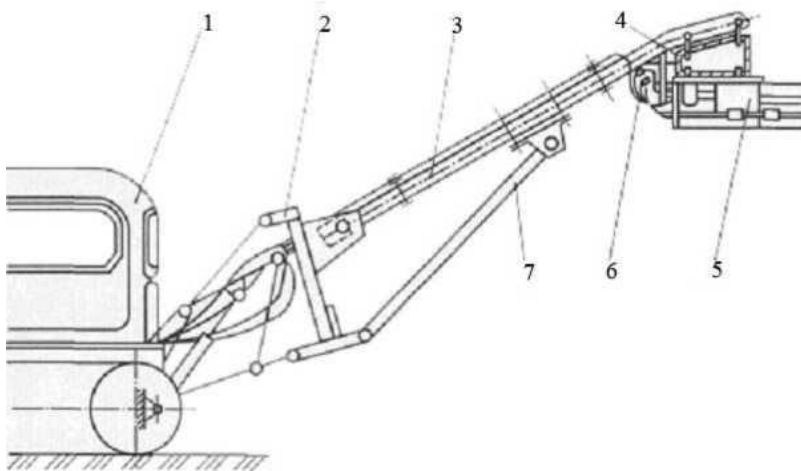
Віброустановка ВСО-1: 1 - трактор; 2 - рама; 3 - стріла; 4 - підвіска; 5 - вібратор; 6 - гідравлічний привід; 7 - штанга
